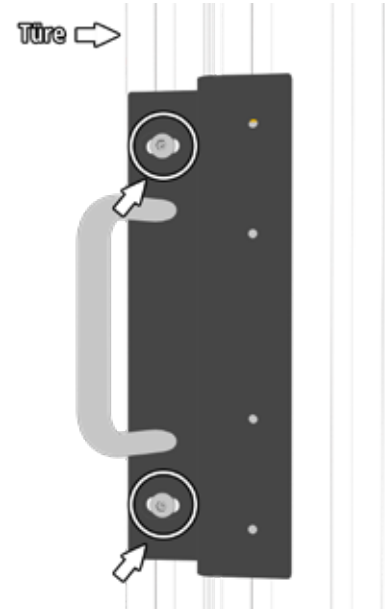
Montageplatte mit Ankerplatte am Profil anbringen und zur Prozesszuhalterung ausrichten. Schrauben M8 x 12 mm Torx festziehen.
